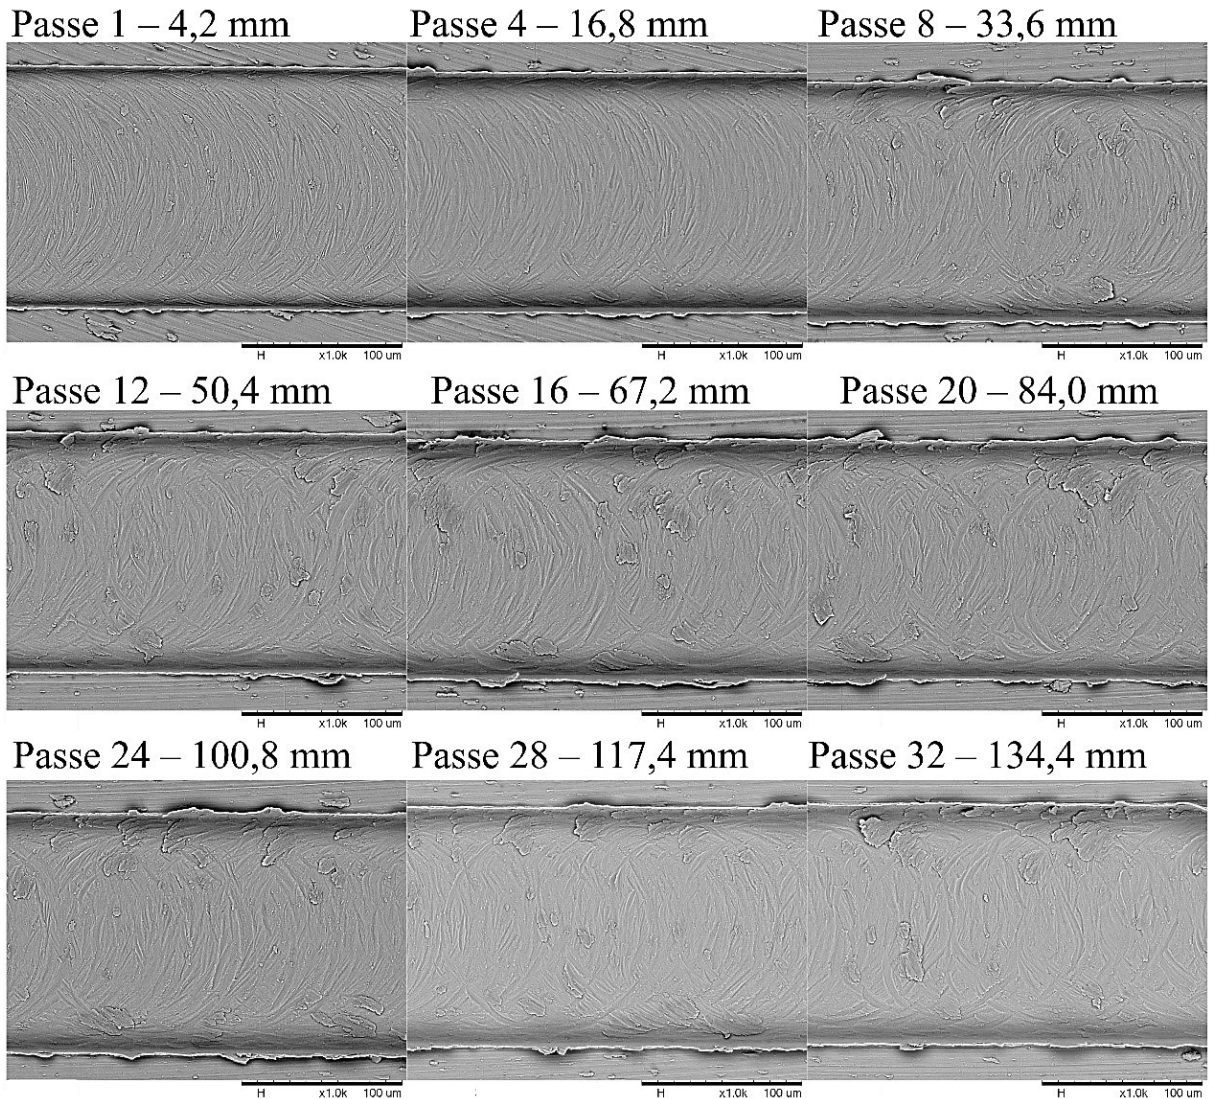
Superfície usinada a seco com microferramenta revestida de DLC
